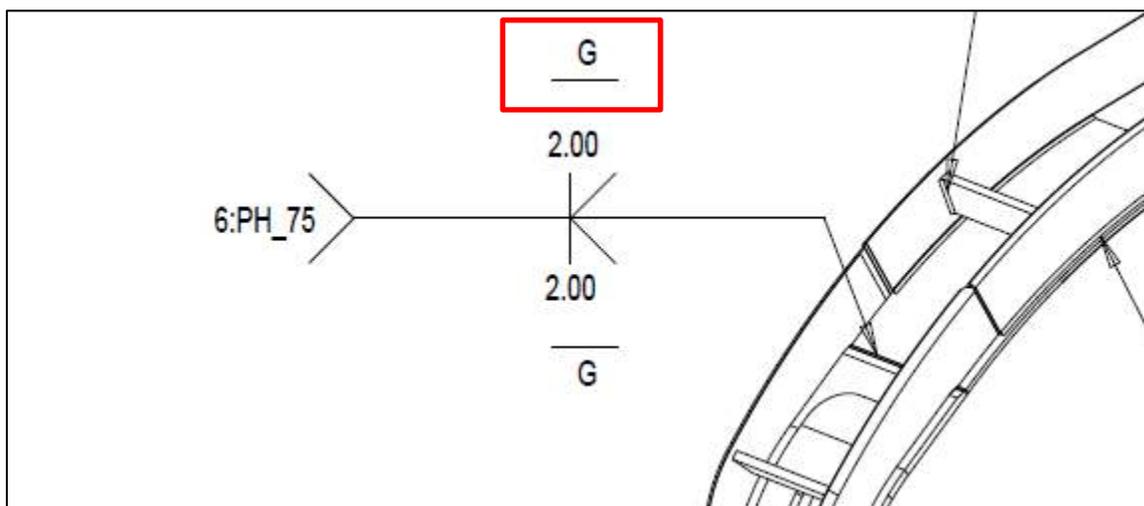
Ejemplo de Nomenclatura de Acabado en Assembly Drawing
